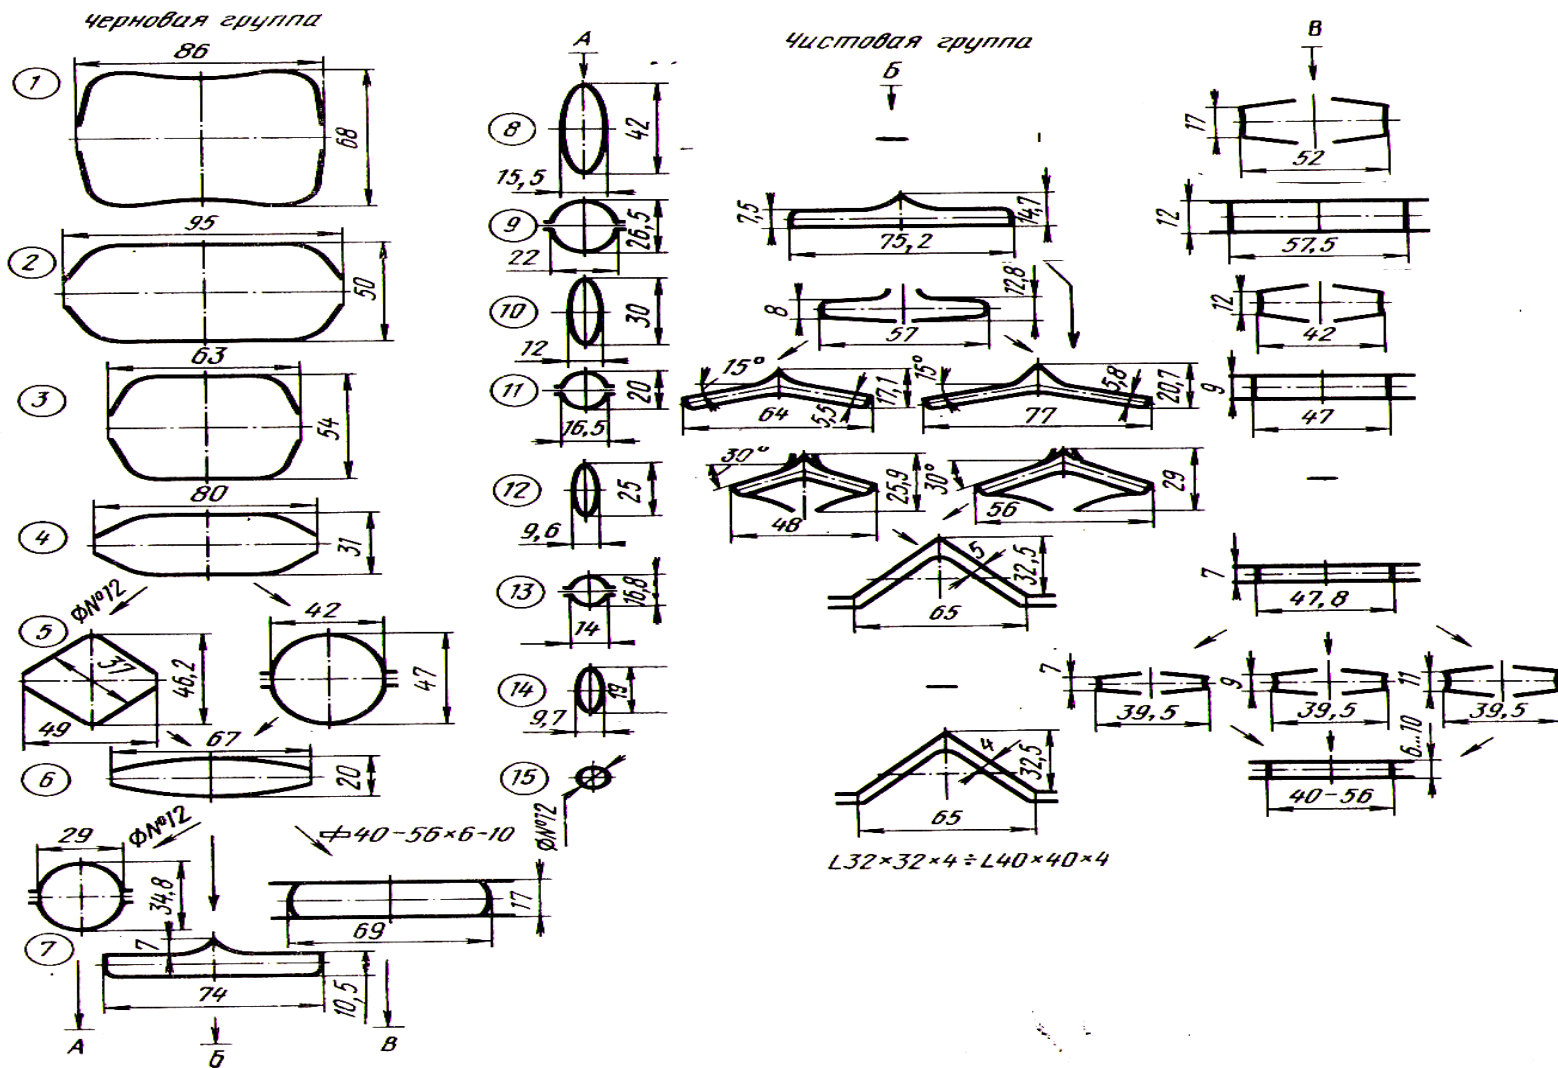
Схема прокатки на непрерывном дробносортовом стане 250
